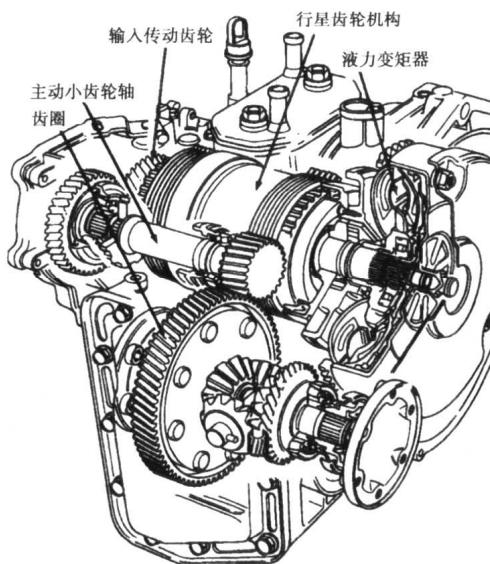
拉维奈尔赫式行星齿轮自动变速器
